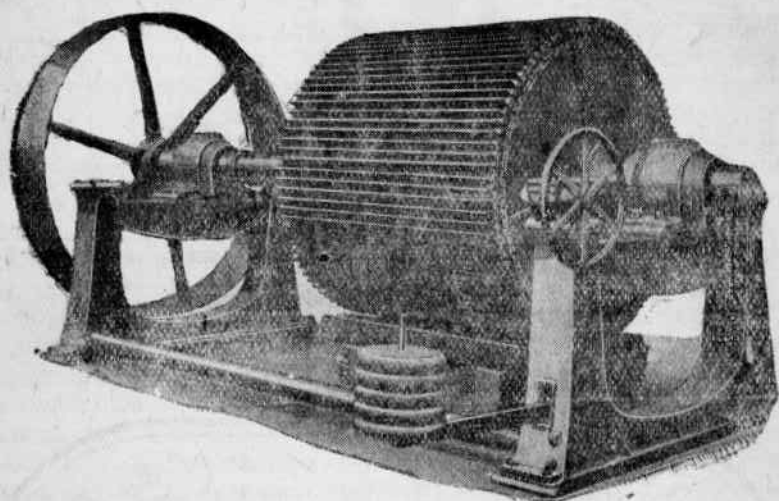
Рольный барабан с ножами; под барабаном планка. Слева шкив, приводящий в движение барабан; справа механизм присадочного приспособления и рычаг с грузом для вылегивания барабана.
